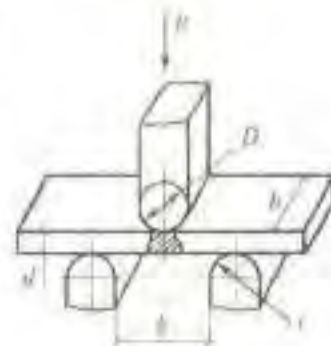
Схеми випробування на статичний згин. D – діаметр трубок
